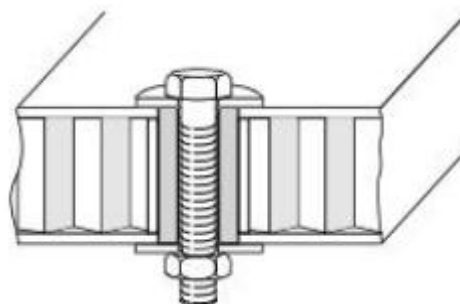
Mechanický insert s ochranným kroužkem na jedné straně [12]
